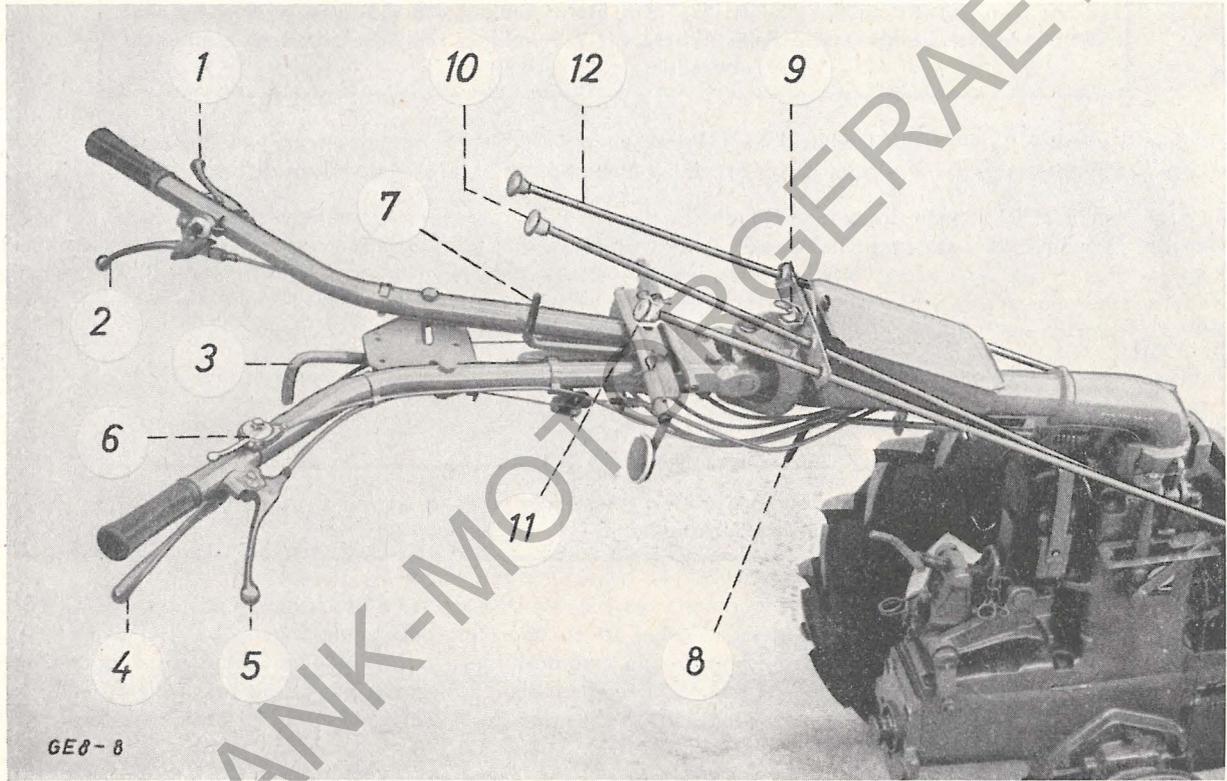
Bedienunggriffe am Holder Universal-Einachsschlepper E 8
